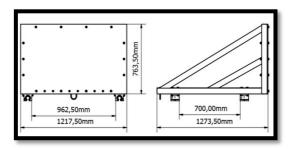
DIMENSIONES DEL TRINEO MÓVIL
